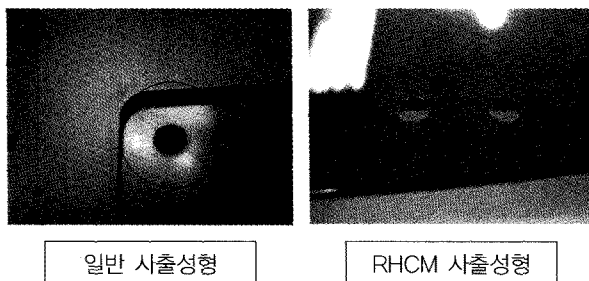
RHCM 가공기술 적용 사례(Weld Line 개선)
